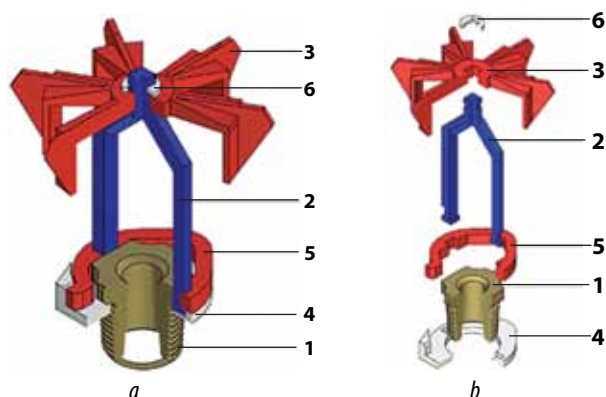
Сборно-разборный ороиситель в собранном (а) и разобранном (b) виде: 1 — штуцер; 2 — держатель; 3 — разбрызгиватель; 4 — кольцевой фиксатор; 5 — дугообразный прижим; 6 — стопорная шайба
